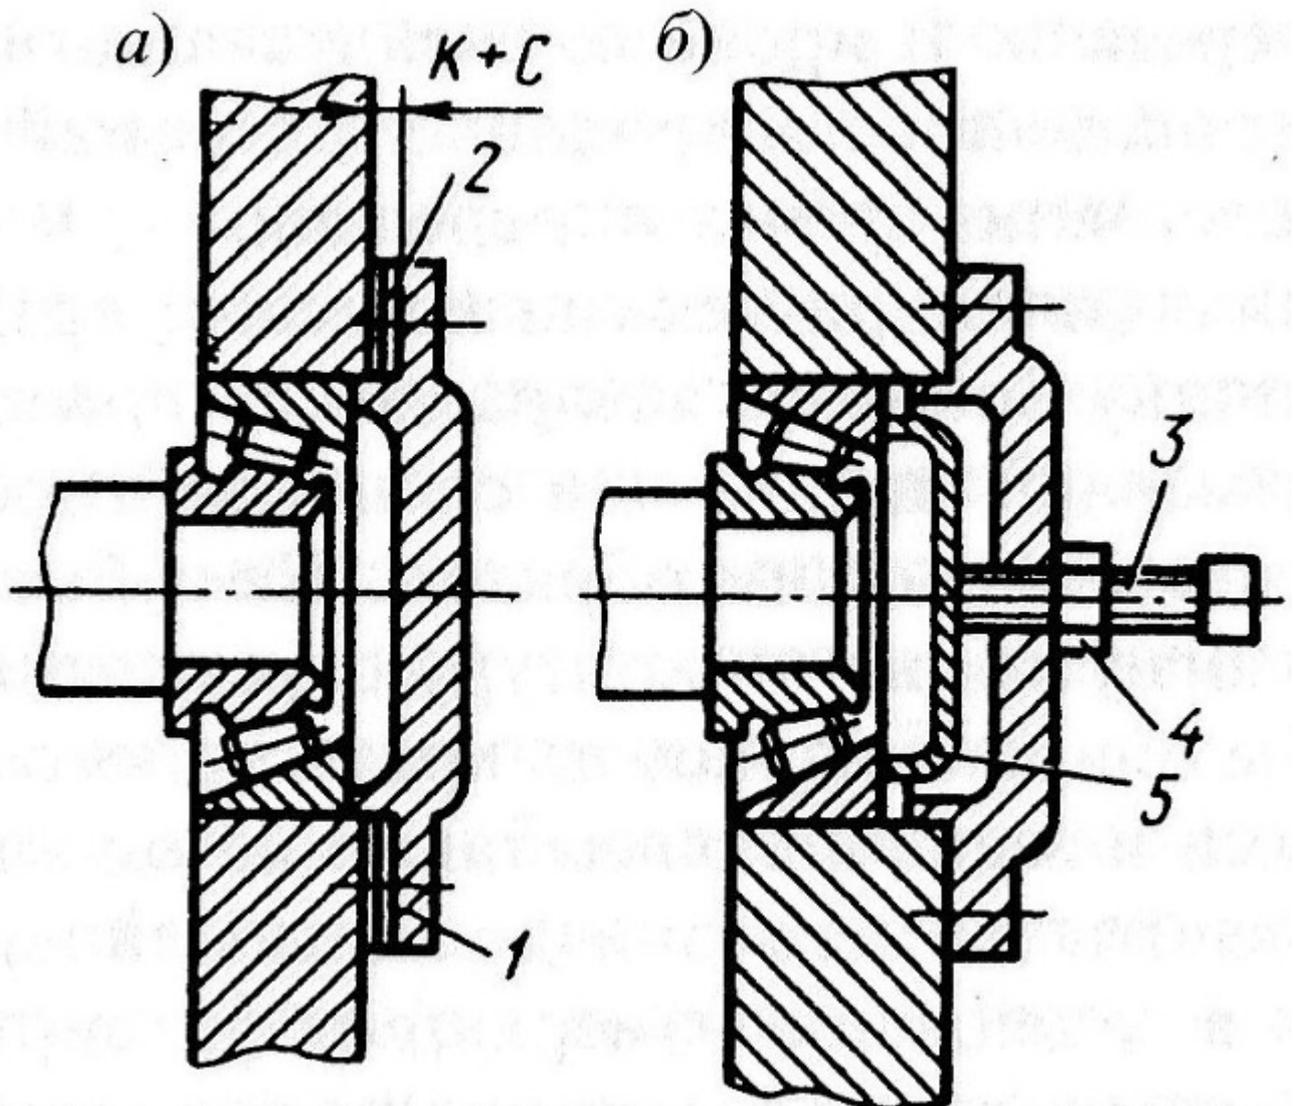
Схемы регулирования зазоров в радиально-упорных подшипниках: а — прокладками; б — винтом; 1 — крышка; 2 — прокладка; 3 — винт; 4 — гайка; 5 — проставка
